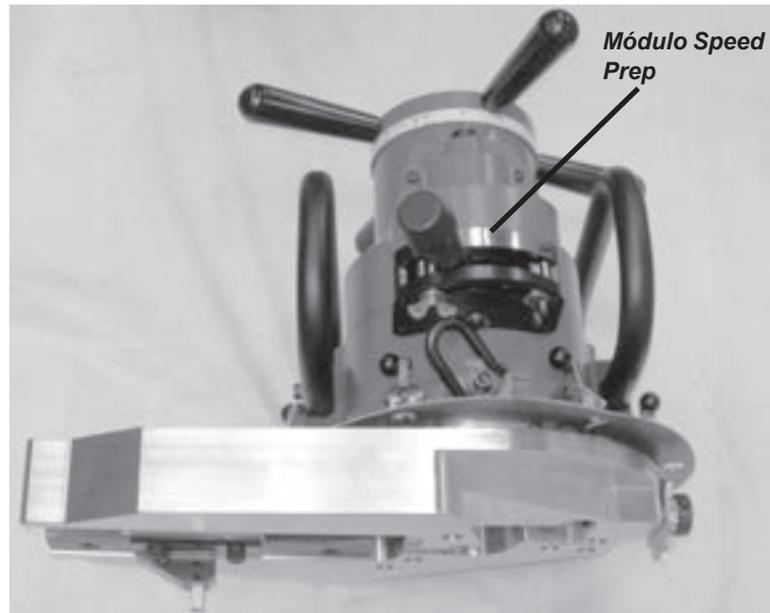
El módulo Speed Prep está instalado en el accionamiento principal para operar el mecanismo de avance para biselado de punta única.
